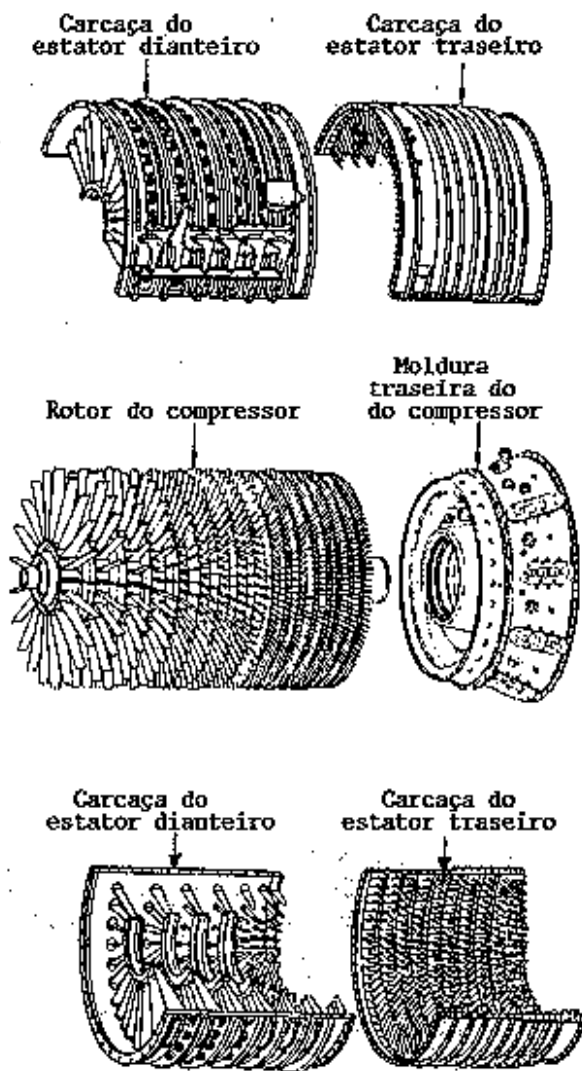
Rotor estator componentes de um compressor de fluxo axial.
